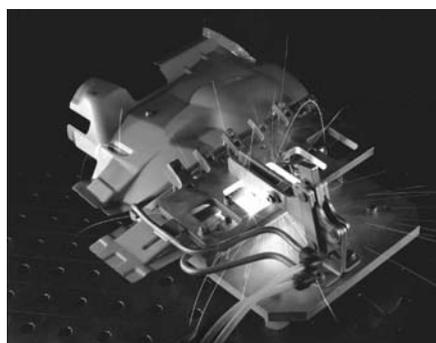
CO₂-Laser-Remoteschweißen in der Fertigung
